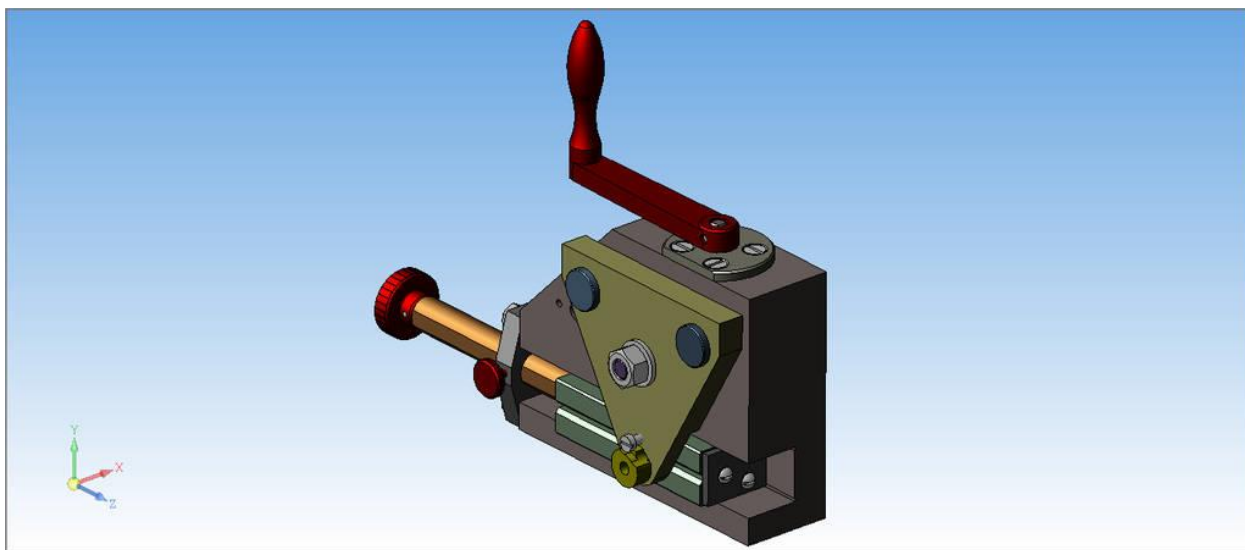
Пример сверлильного приспособления, 3D-модель
